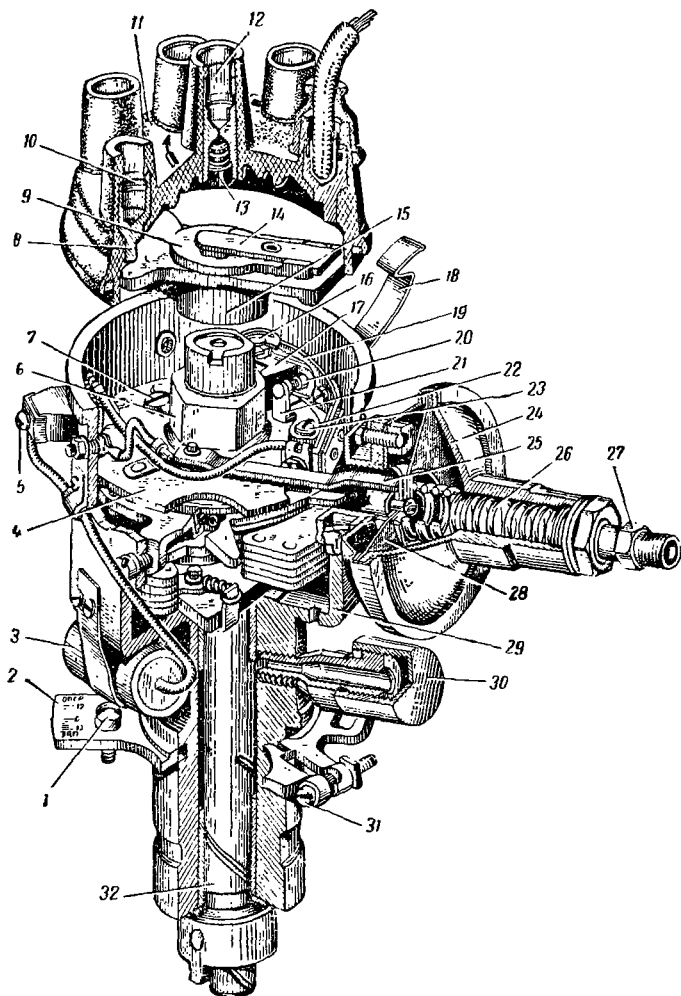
Прерыватель-распределитель двигателя ЗИЛ-120.
